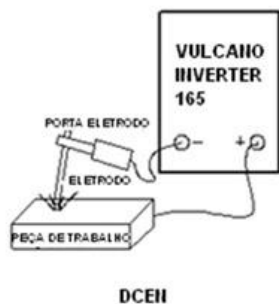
Conexão negativa para soldagem com eletrodo revestido
